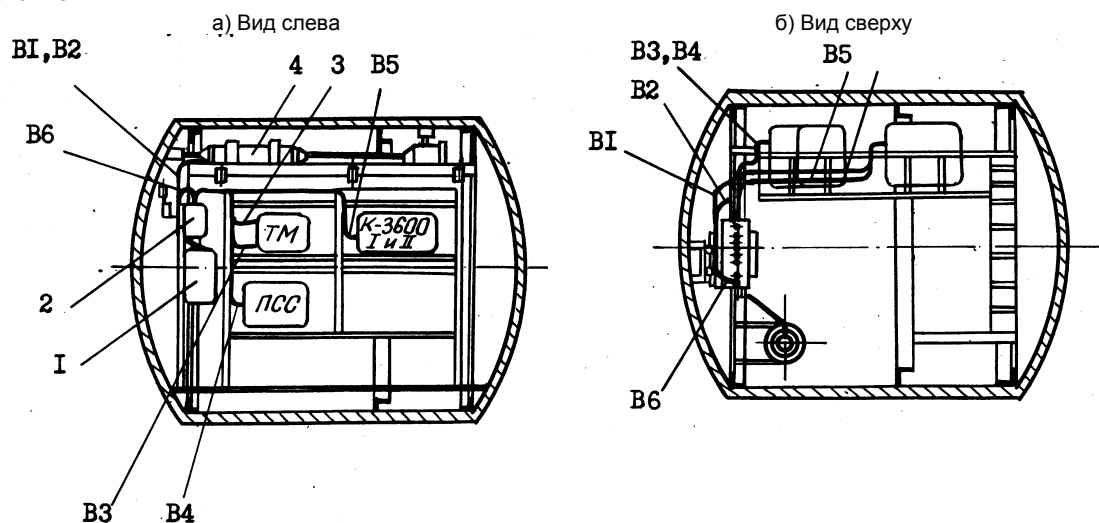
Подключение воздухопроводов от УСКД-1М к кабелям типа КМ-4 и от РУ-6ДМ к контейнерам СП К-3600 (К-1920 П) 1 — УСКД-1М; 2 — РУ-6ДМ; 3 — кабель КМС-2; 4 — соединительная коаксиальная муфта; В1 — В6 — воздухопроводы
